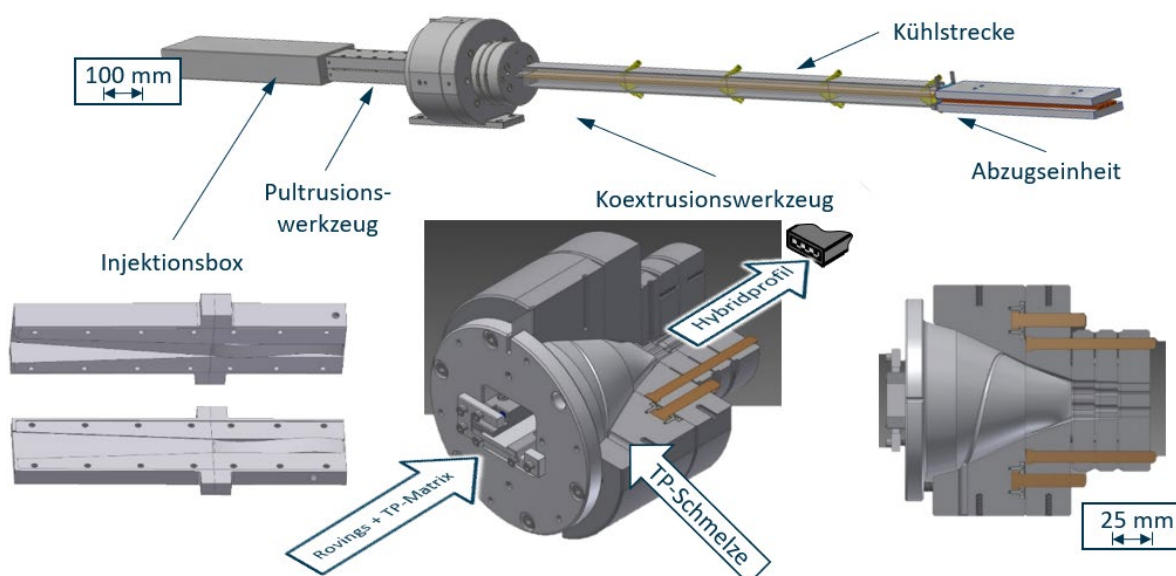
Werkzeugtechnik für den kombinierten Pultrusions- und Extrusionsprozess
